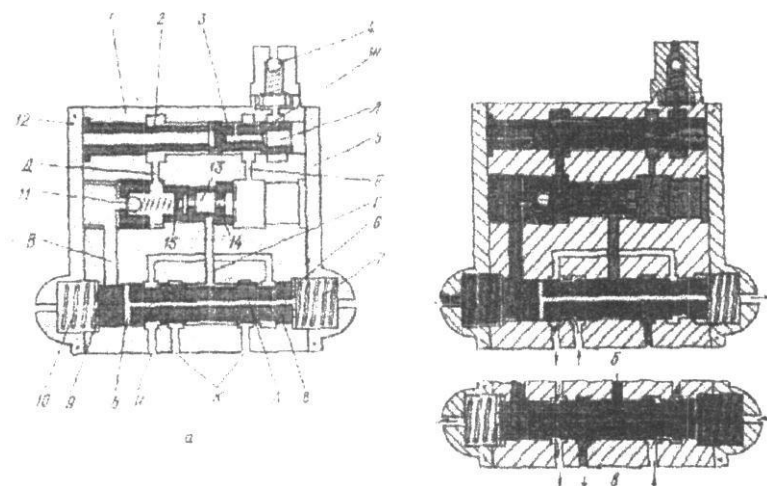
Схема работы усилителя потока: 1- корпус; 2- ограничительная втулка; 3- отсечной клапан; 4 и 11 -обратный клапан; 5 и 12- крышка; 6 и 9 - шайба; 7-10 - пружина; 8 - золотник; 13- отражатель; 14 и 15 - дроссель; А - осевое сверление золотника; Б -радиальное сверление золотника; В и Г - сверления, связывающие полость золотника с полостью дросселей; Д и Е -
